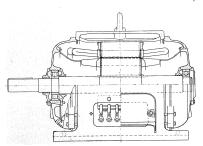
Общий вид (разрез) электродвигателя А 8-го габарита
